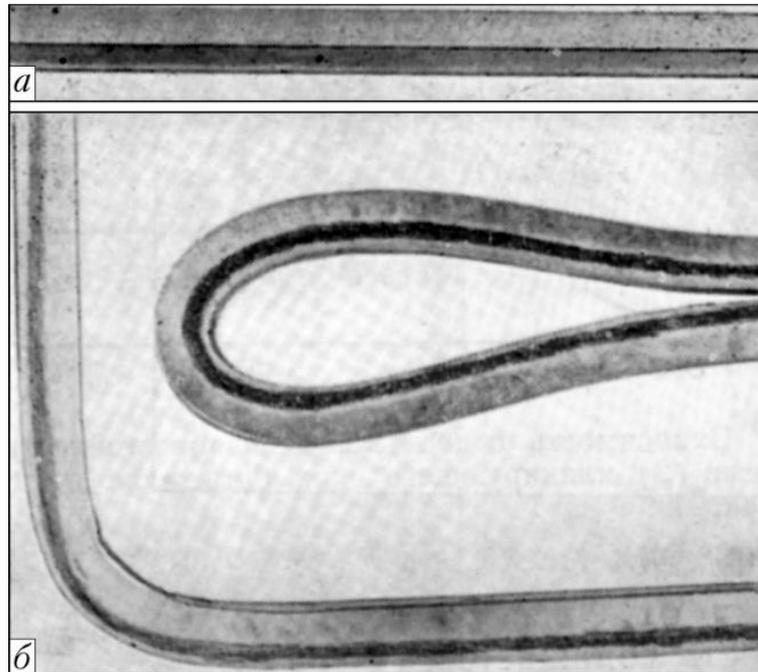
Макрошлифы биметалла сталь 45 + ПГ-С1 после прокатки (а) и штамповки (б)
